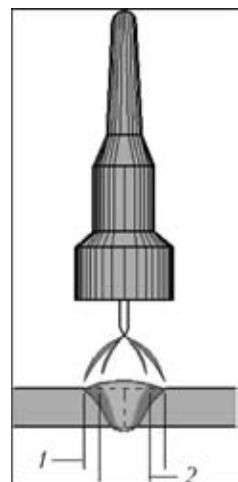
Схема геометрии сечения металла шва при сварке ТИГ с непрерывной (1) и импульсной (2) дугой
